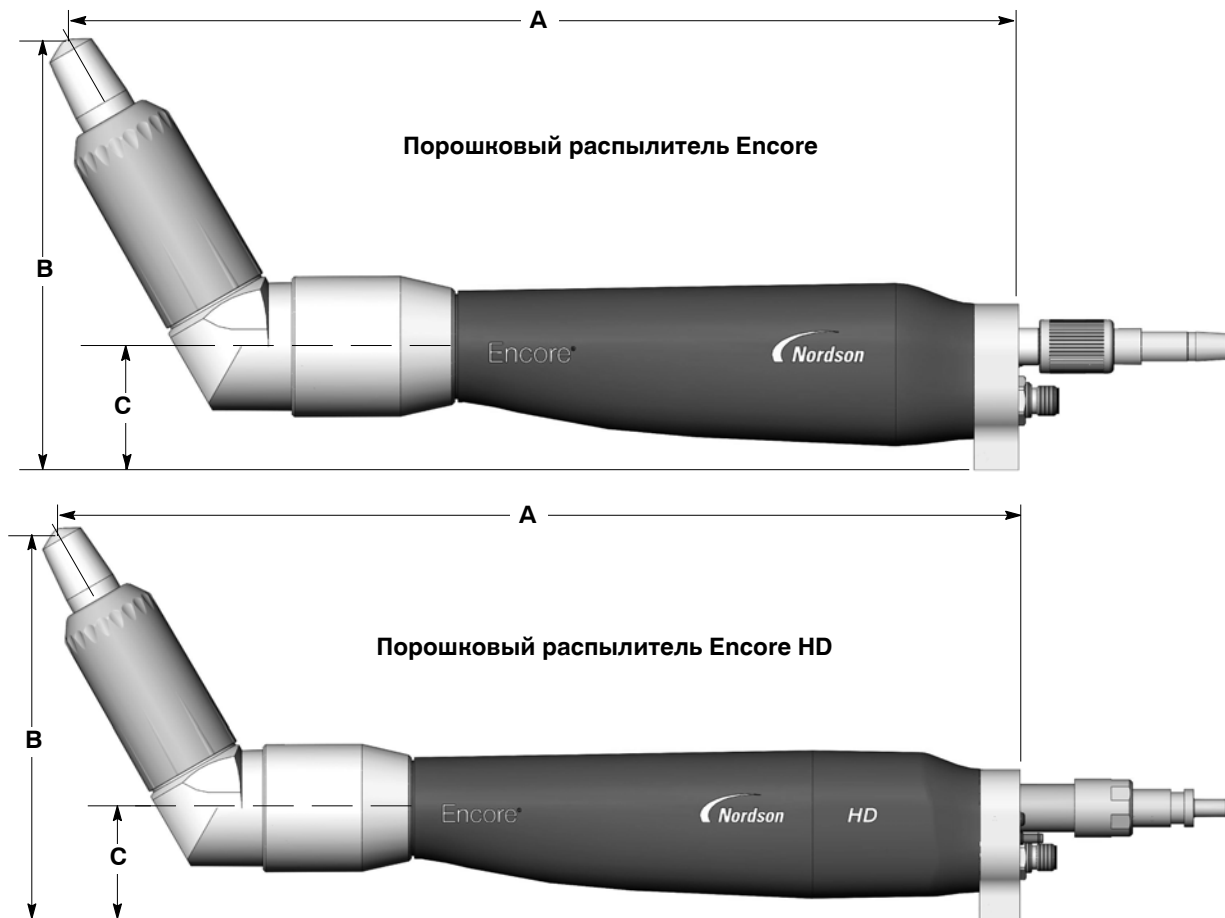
Порошковые распылители Encore и Encore HD с угловой насадкой Encore (показана 60-градусная насадка)
